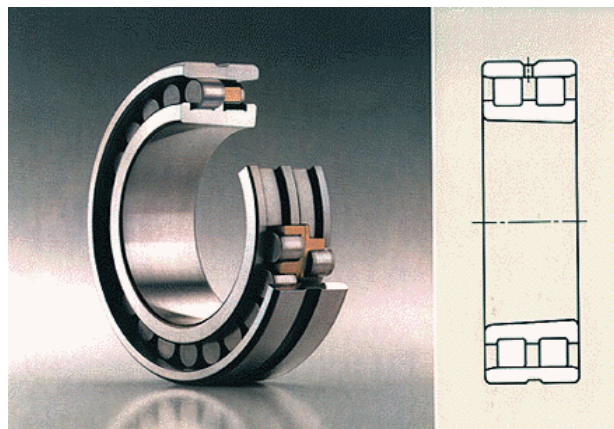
Rodamiento de rodillos cilíndricos de dos hileras
